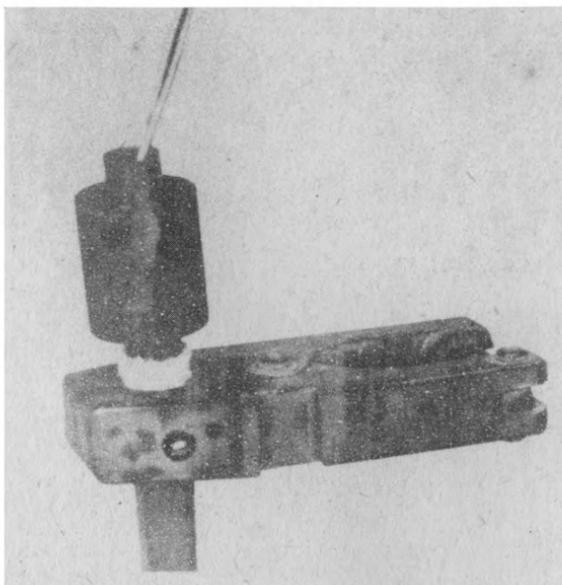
Зведение присадочного прутка из алюминиевой проволоки в кокиль термитного патрона марки АС при сварке алюминиевой жилы кабеля со стальным стержнем
